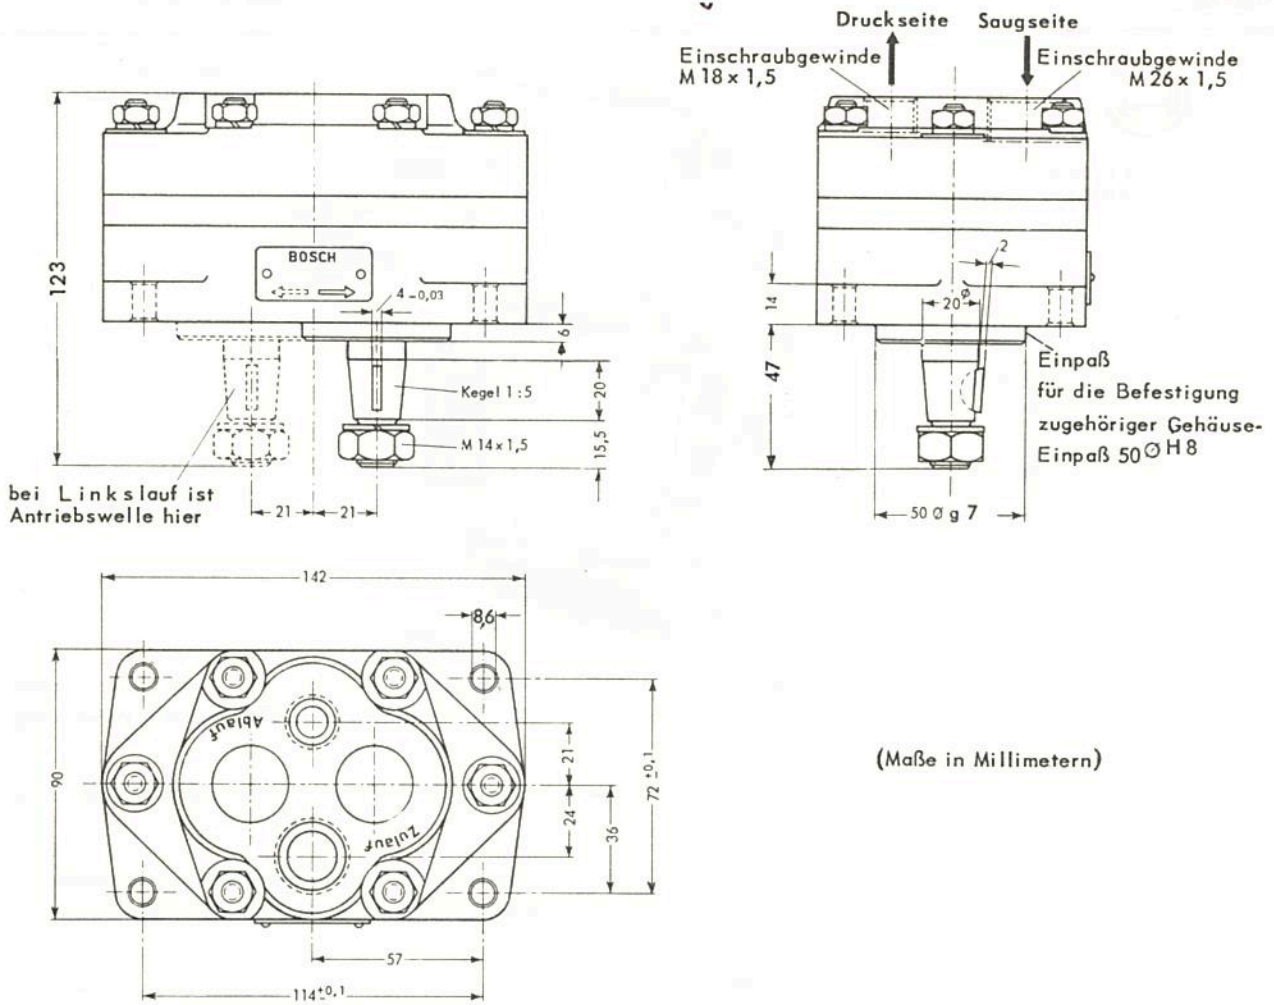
Maßzeichnung der Hydraulik - Pumpe HY/ZE 16 CR(L)..
